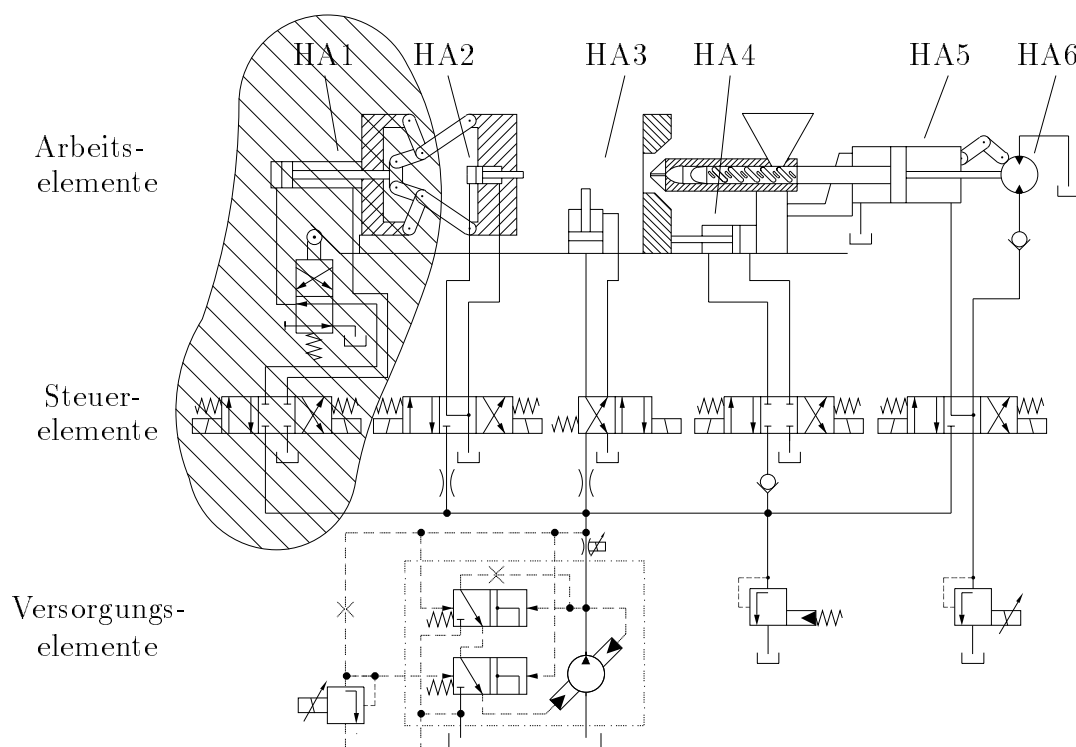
Hydraulisch angetriebene Kunststoff-Spritzgießmaschine
